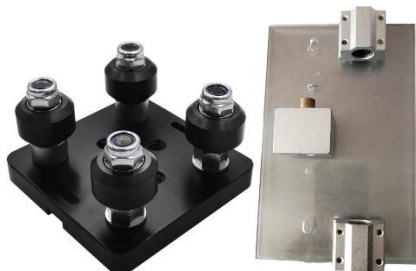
Placa de rodamientos y pieza de unión. Fuente: Propia
